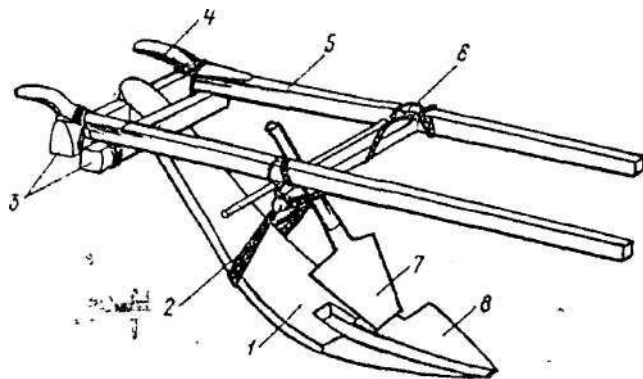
Великорусская соха с перекладной полицей: 1 - рассоха; 2 - подвязка (пружина); 3 - бруски; 4 - рукоятка; 5 - оглобля (обжа); 6 - поперечина; 7 - полица; 8 -ральник.
